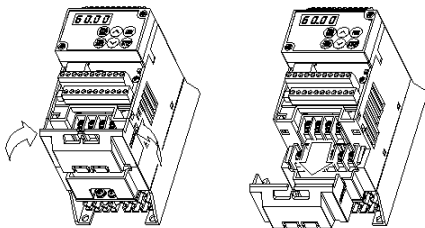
Порядок снятия крышки клеммной коробки блока главной цепи
